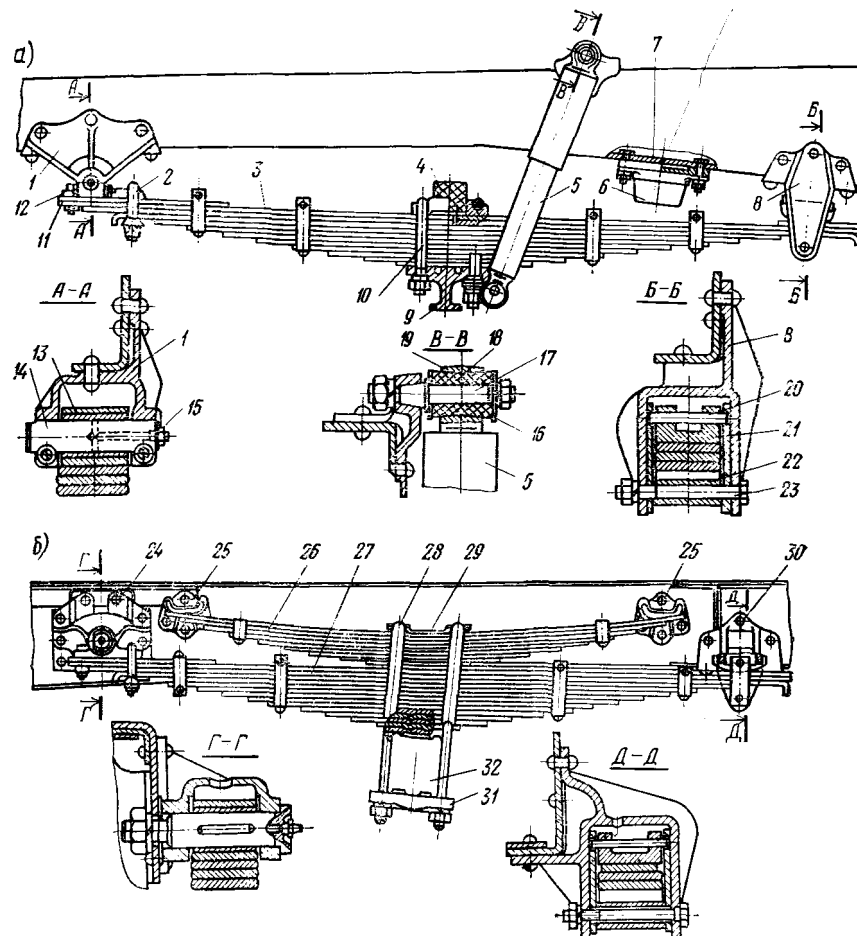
Рессорная подвеска автомобиля ЗИЛ-130:
